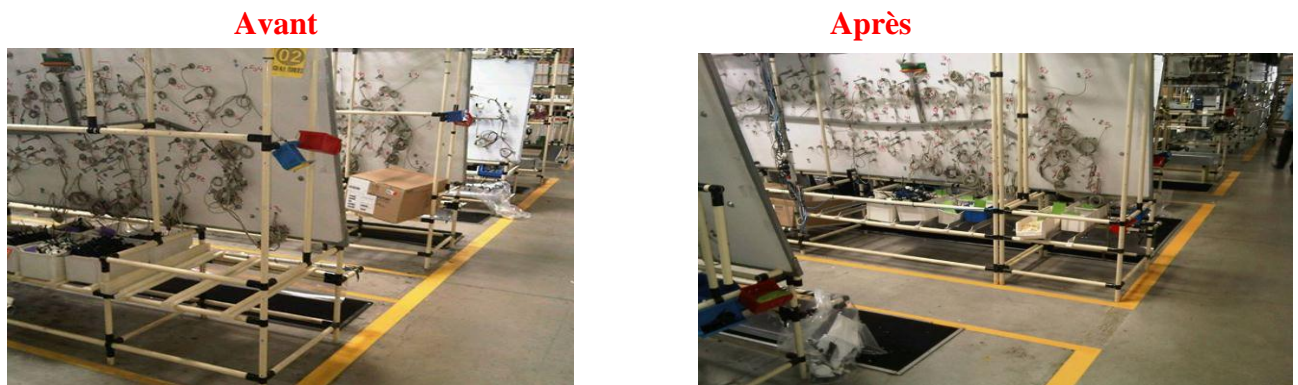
Tableaux de sub assembly avant et après l'amélioration
